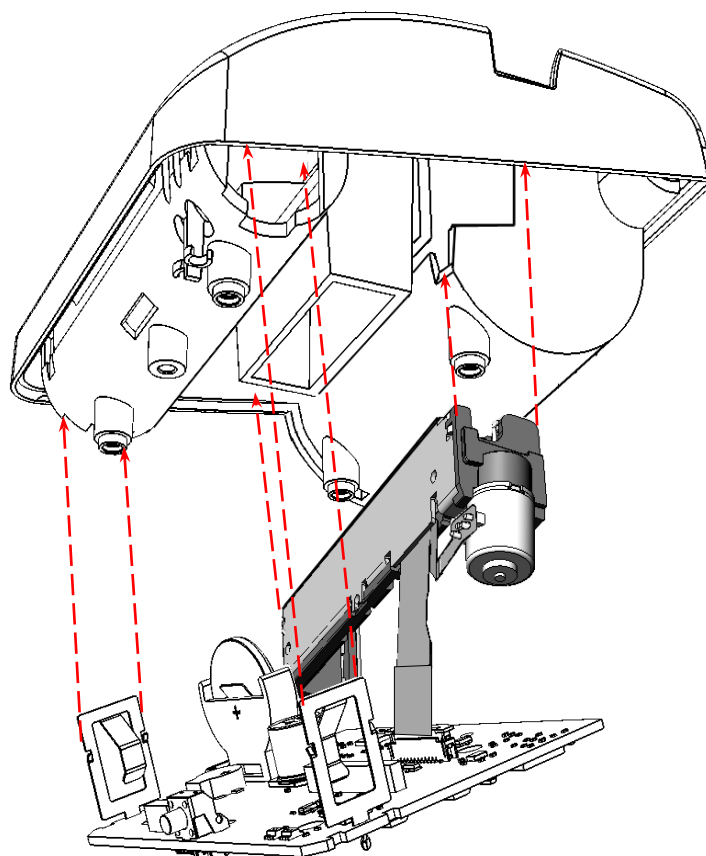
Установка конструкции ТПГ–БУ в верхнюю часть корпуса ККТ.
